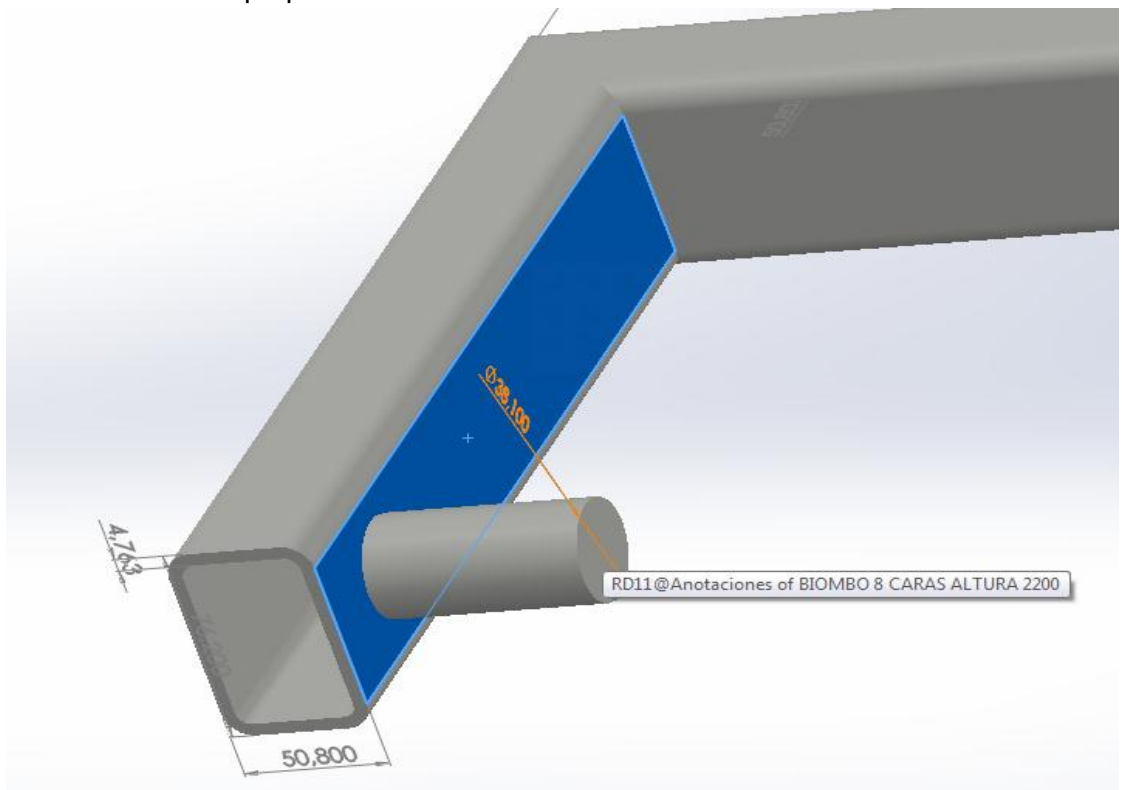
Detalle sujeción base giratoria a columna en el extremo opuesto
